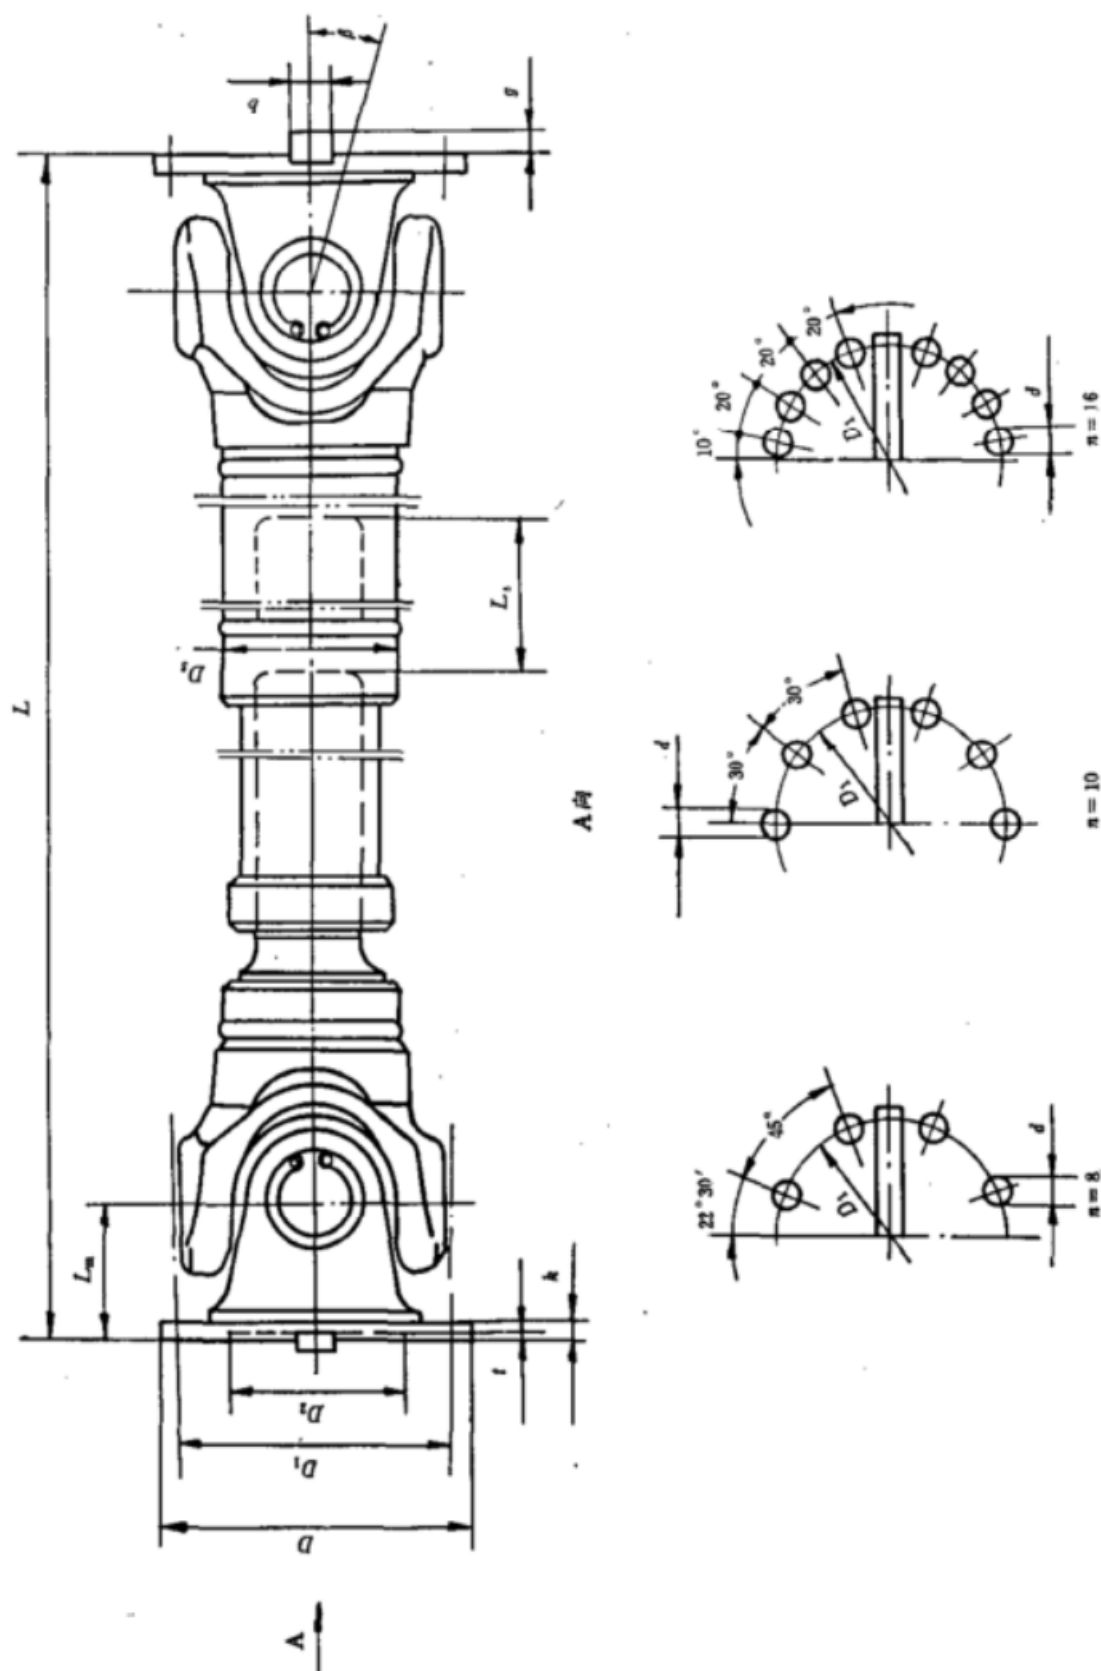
CH 型——长伸缩焊接式万向联轴器
